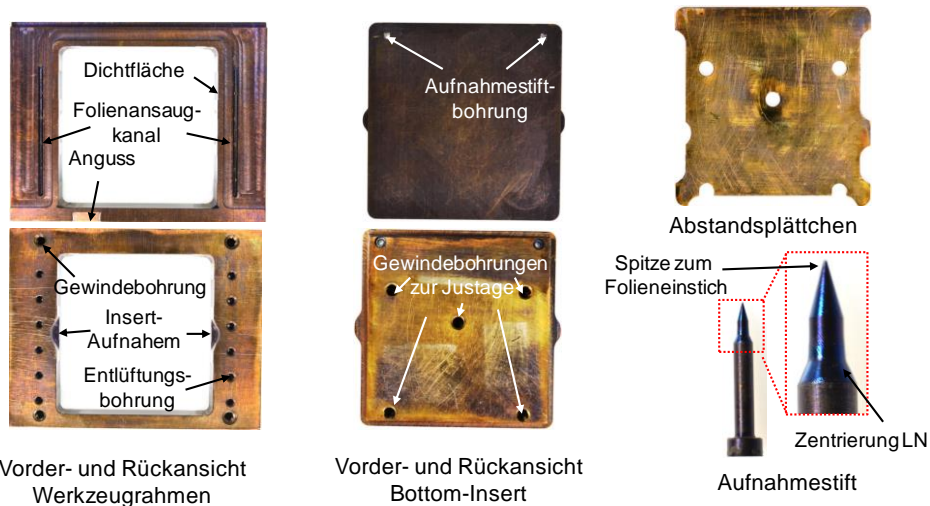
Bottom-Werkzeugelemente vereinzelt dargestellt.
